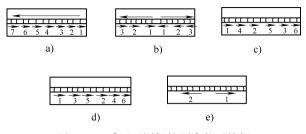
采用不同焊接顺序的对接焊 a)逐步退焊法 b)分中逐步退焊法
